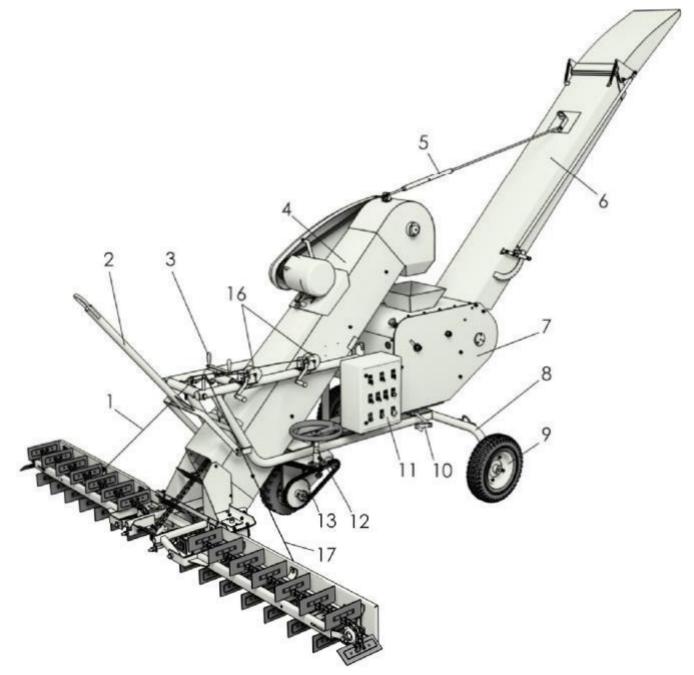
Основные сборочные единицы метателя зерна МЗС-90-20-01М
